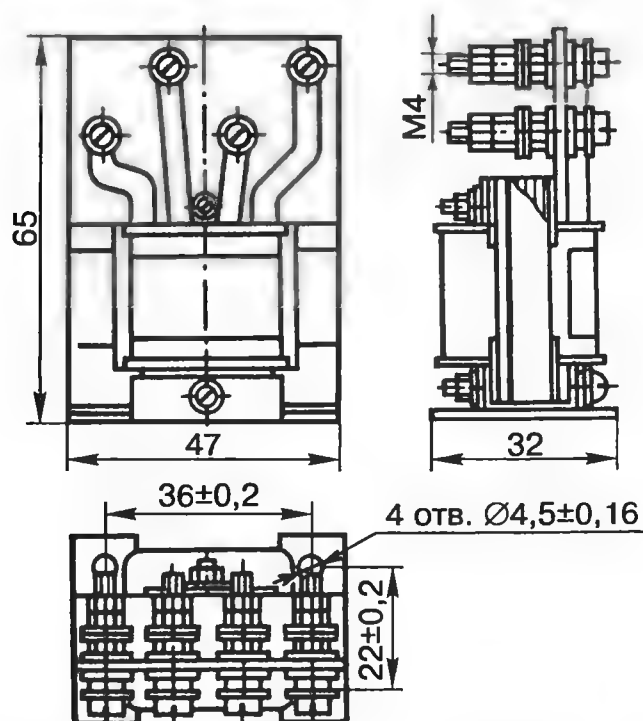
Присоединительные и габаритные размеры трансформатора РТ-3
